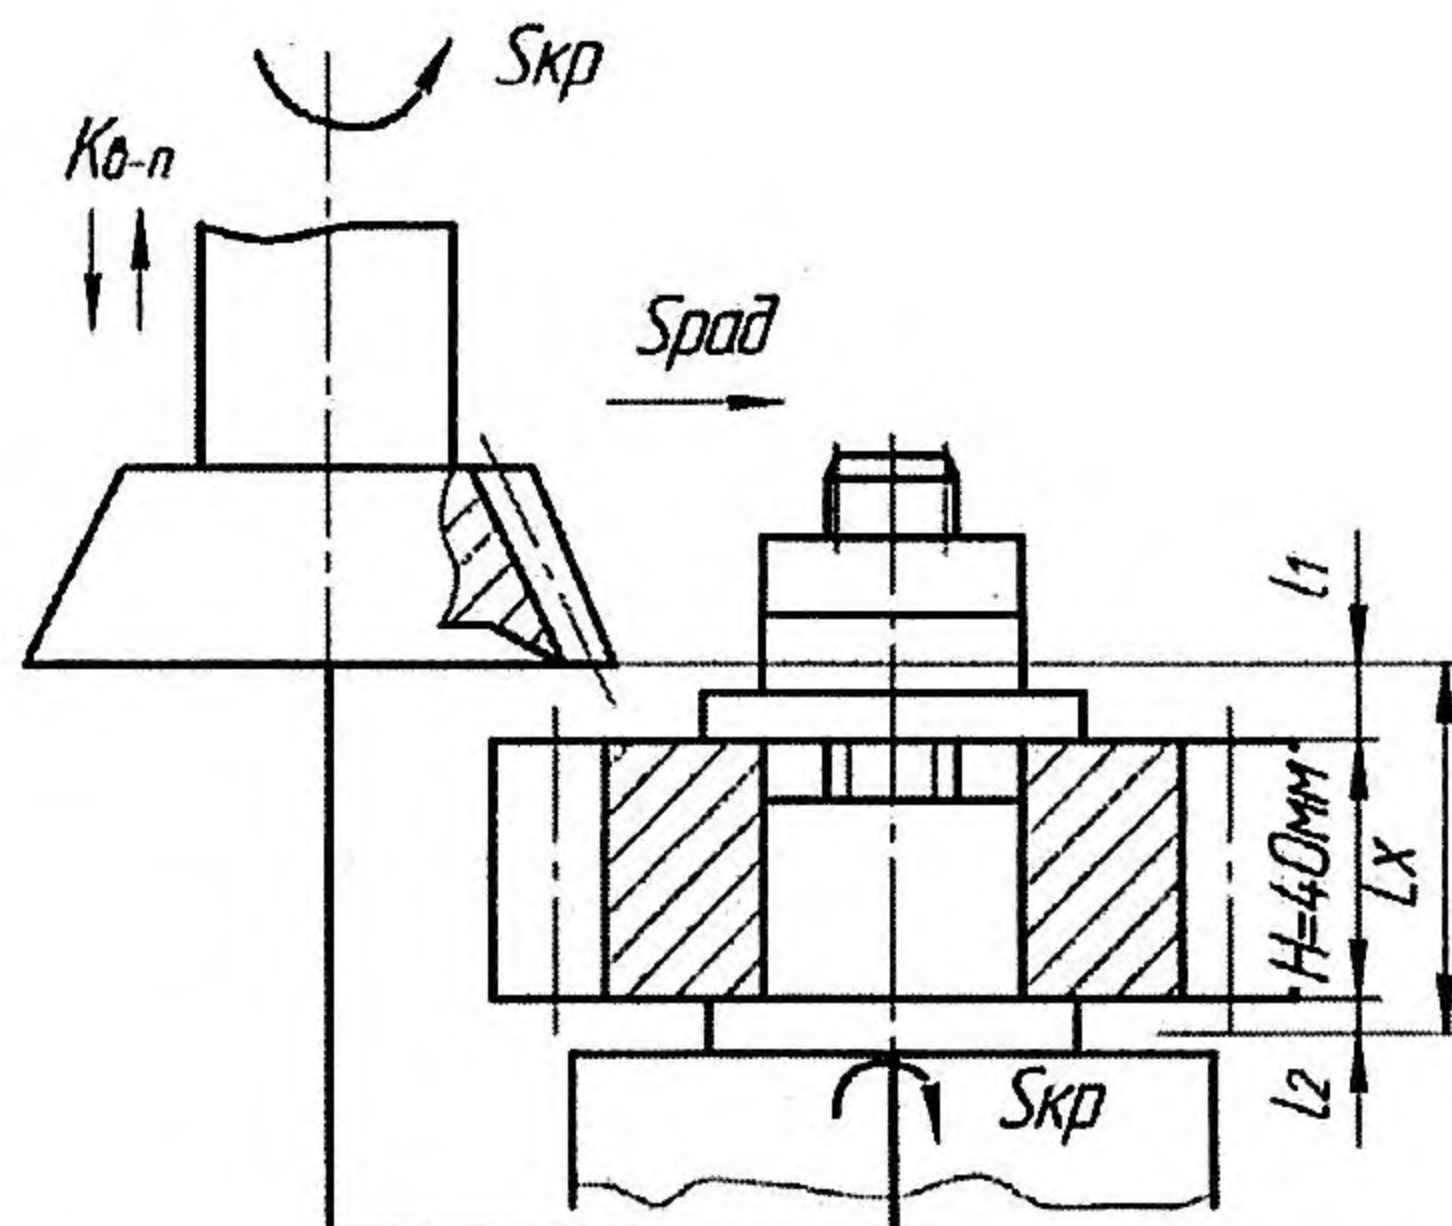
Схема обработки колеса на зубодолбежном станке
